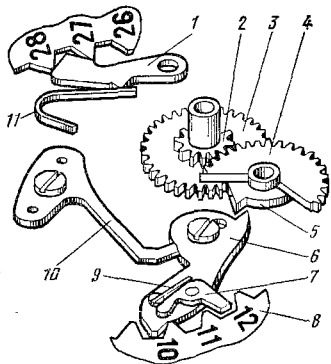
Кинематическая схема календарного устройства часов «Слава» 2414:
